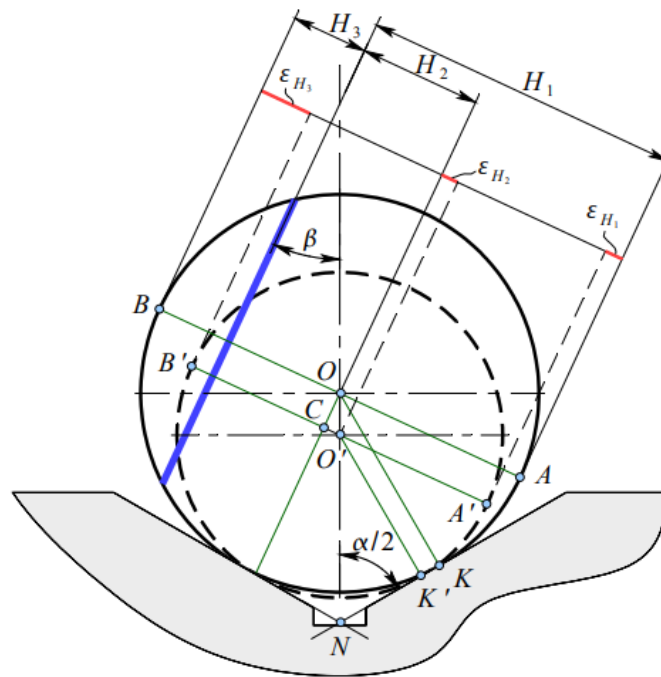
Розрахункова схема (для операції фрезерування лиски)
